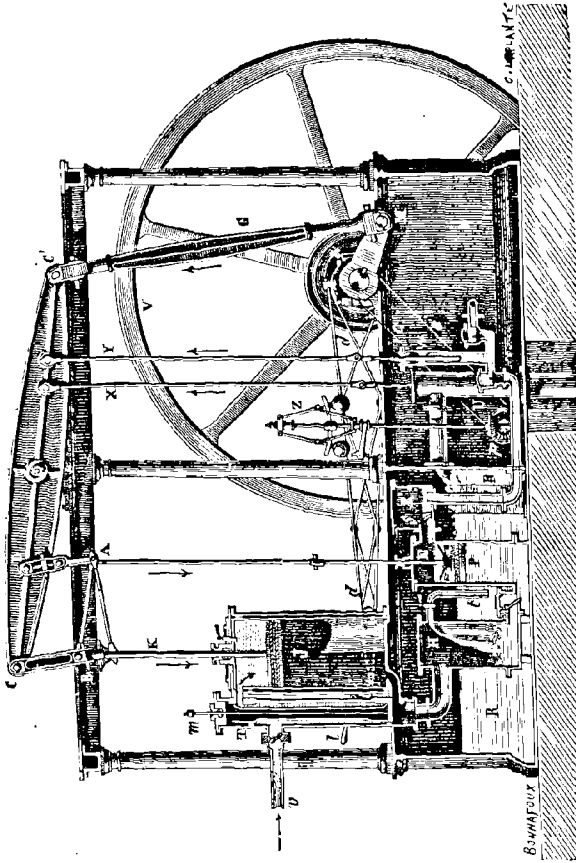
Coupe d'une machine à vapeur à condenseur et à balancier.
